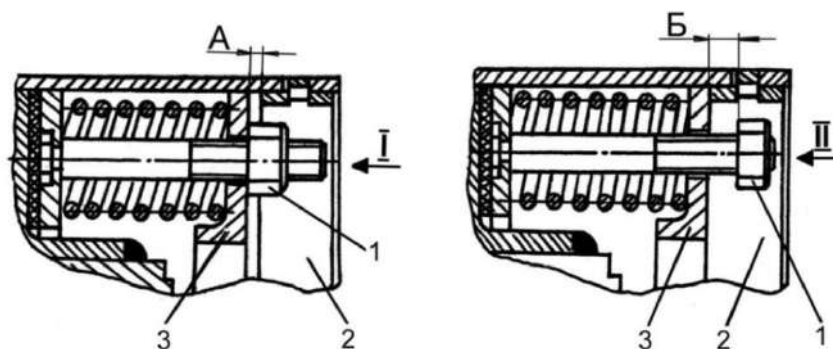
Установка положения шпонок на валах привода вальцев жатки
